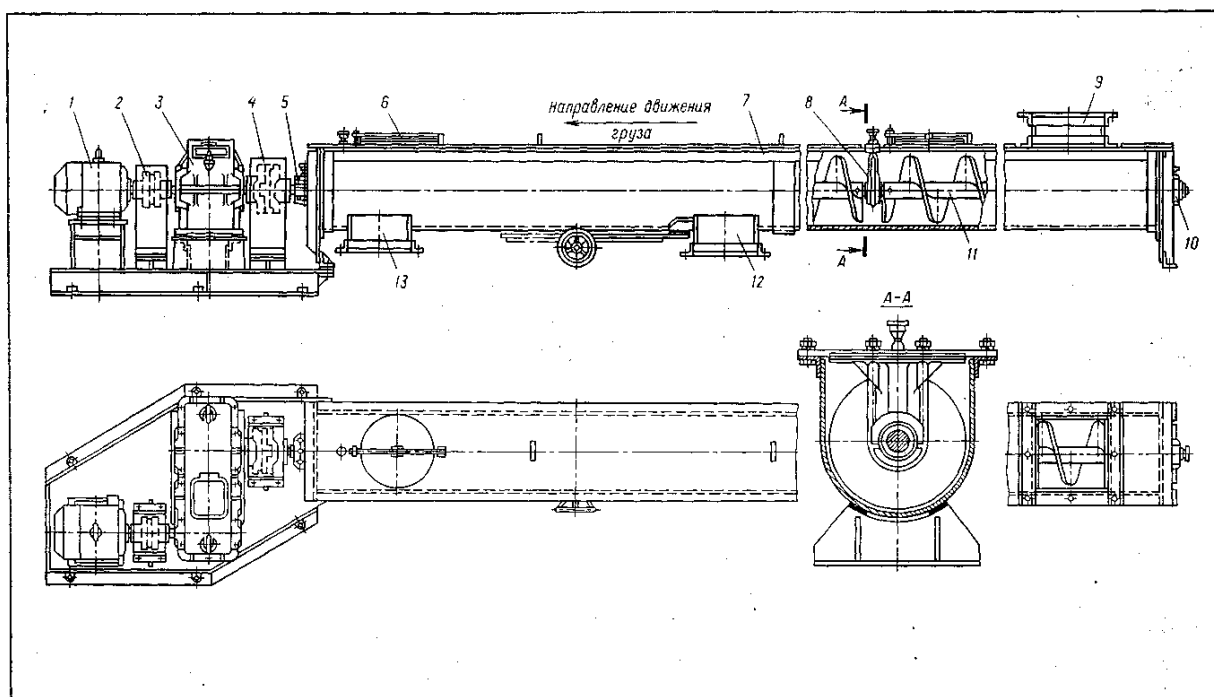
Гвинтовий конвеєр: 1 — електродвигун; 2 — сполучні муфти; 5 — редуктор; 5 — головний підшипник; 6 — оглядовий люк; 7 — жолоб; 8 — проміжний підшипник; 9 — завантажувальний патрубок; 10 — задній підшипник; 11 — вал із гвинтом; 12 — проміжний розвантажувальний патрубок; 13 — передній розвантажувальний патрубок.
